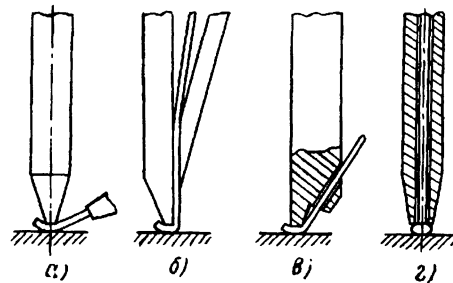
Рабочий инструмент для термокомпрессионной сварки
